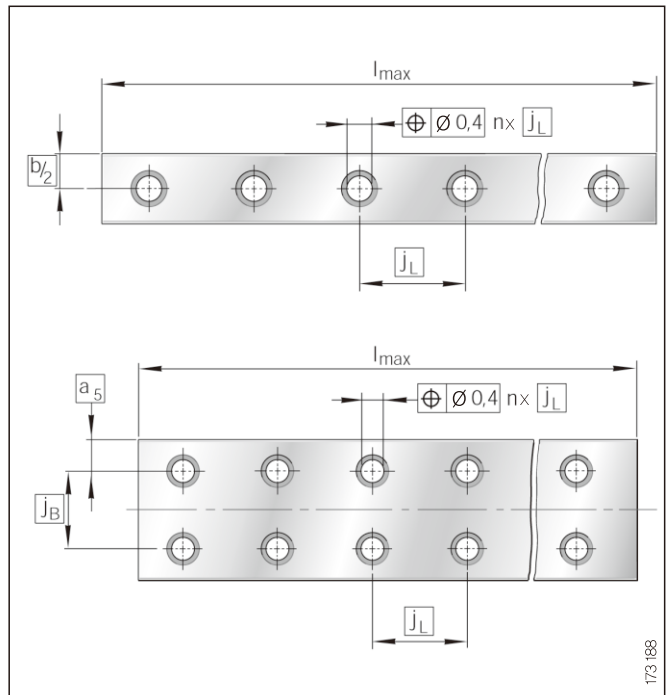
가이드웨이의 위치 및 길이 공차 - DIN ISO 1101에 의거하는 구멍 패턴
